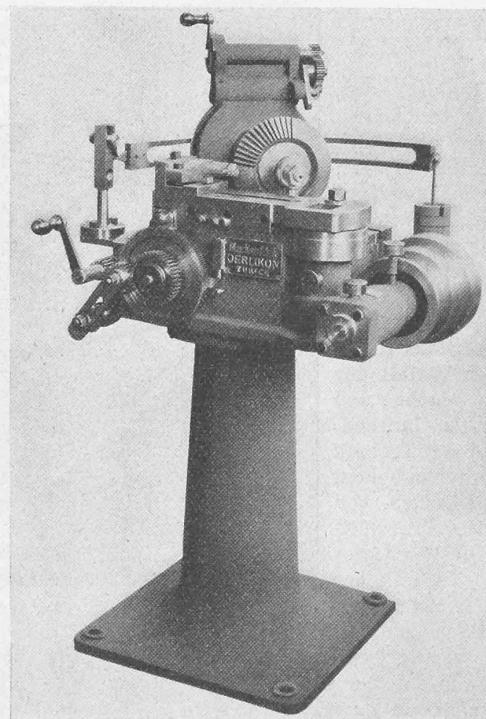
Räderhobelmaschine für Kegelräder bis 200 mm Durchmesser.
